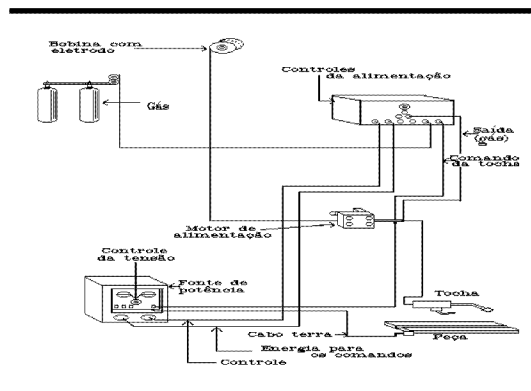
Sistema Esquemático para Soldagem com Eletrodo Tubular.
